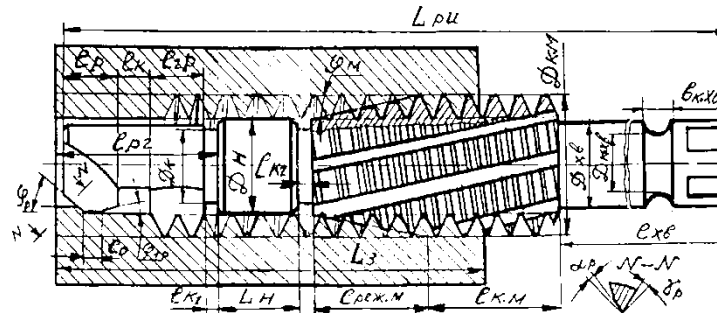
Схема, характеризующая способ нарезания внутренней резьбы комбинированным инструментом «Резец-гребёнка-метчик с направляющей»
